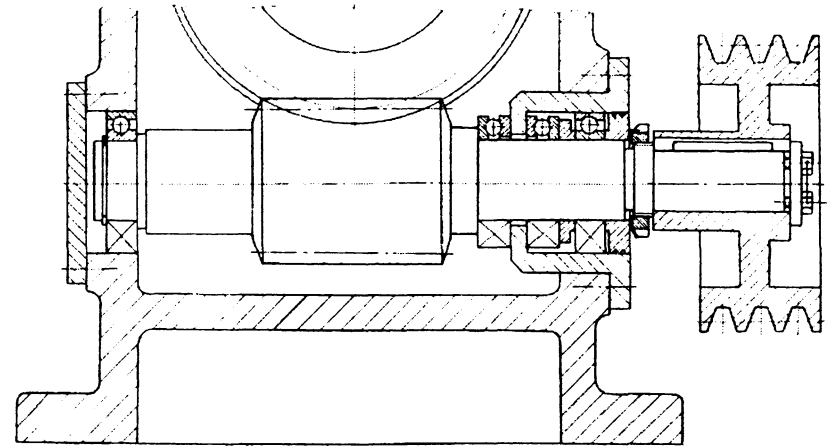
Вал-червяк червячно-цилиндрического редуктора:
